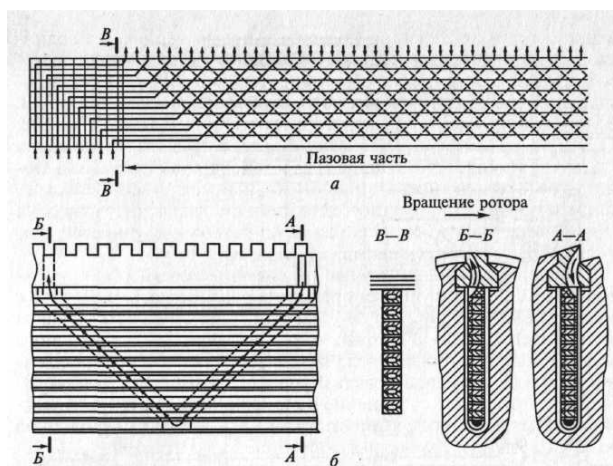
Схема охлаждения роторов турбогенераторов серий ТВФ и ТВВ: а — общая схема охлаждения; б — элементарный путь охлаждающего газа; А—А, В—В — разрезы пазов ротора; В—В — разрез по пазу ротора в торцевой части
